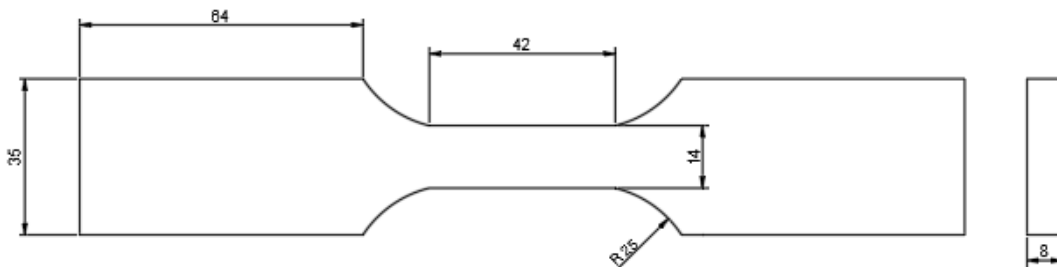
Exemple d'éprouvette de fatigue (dimensions en mm)
